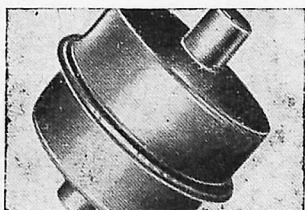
Вакуумная газодуговая сварка алюминия с отбортовкой.
